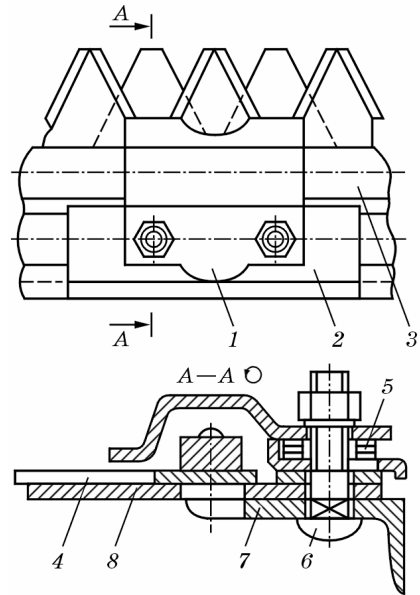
Двоножовий різальний апарат з одним рухомим ножем:
